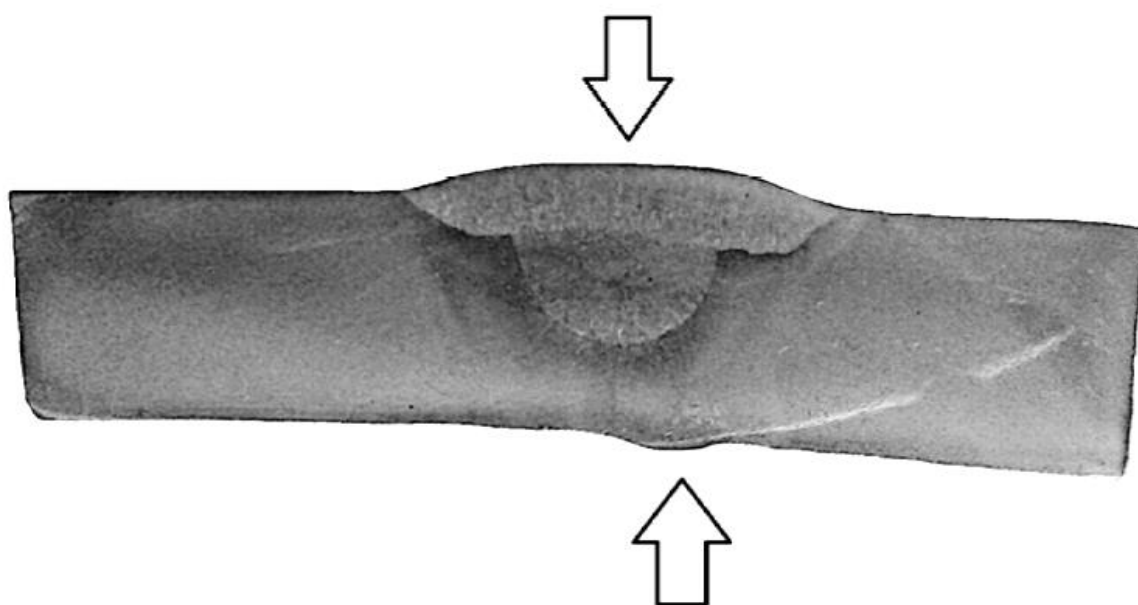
Макрошлиф сварного шва и линия смещения
